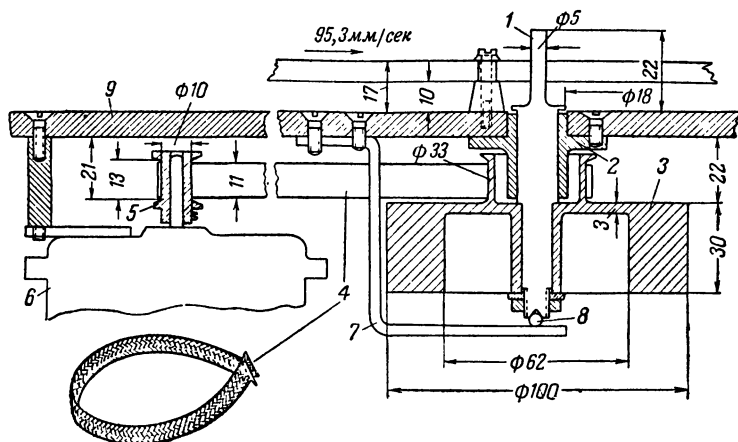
Конструктивное устройство ведущего узла трехмоторного магнитофона. 1 — ведущий вал; 2 — втулка; 3 — маховик; 4 — плоский пассик; 5 — шкив электродвигателя; 6 — ведущий электродвигатель 1 200 об/мин; 7 — опорная скоба; 8 — опорный шарик; 9 — панель лентопротяжного механизма.
